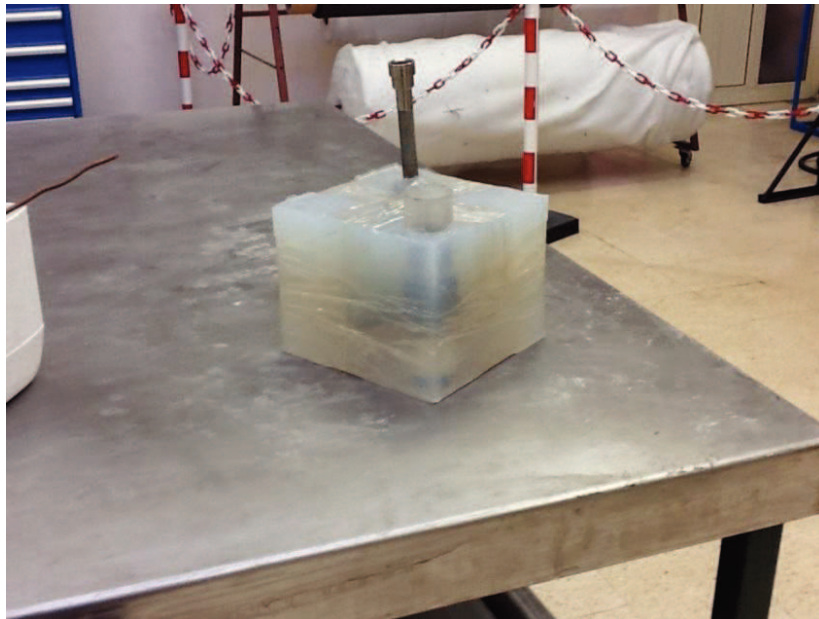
Molde protótipo em silicone (Vacum Casting)
